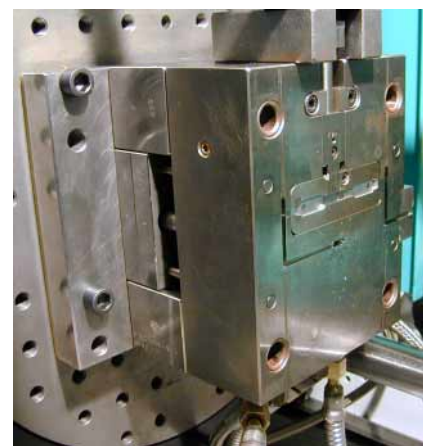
Auswerferseite des geöffneten Werkzeuges mit ausgefahrenem Schieber.
